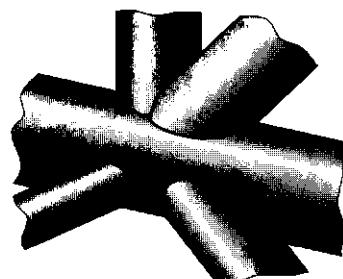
Сварной узел с изменяющимся типом сварного соединения
